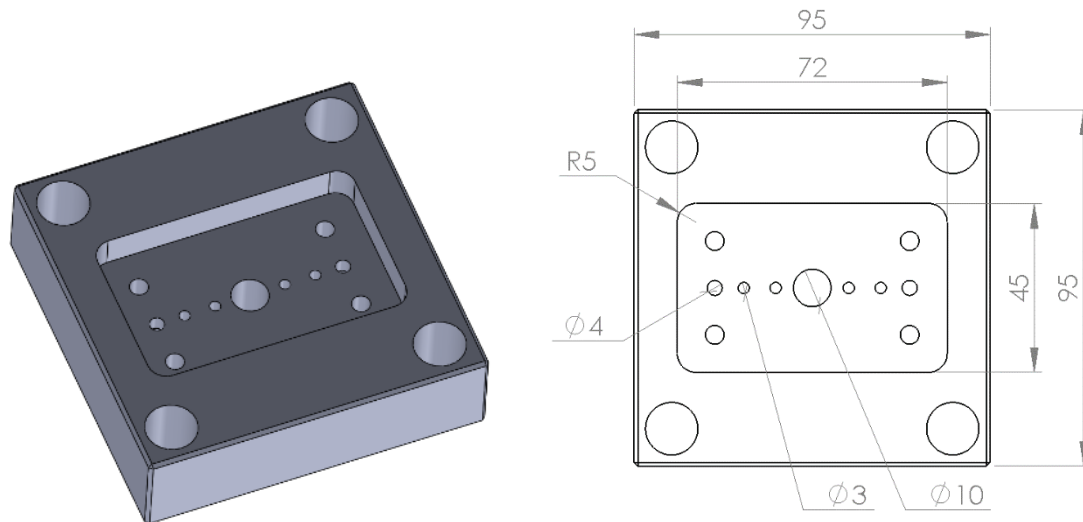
Esquerra: Model CAD del MUD. Dreta: Vista en planta del MUD (Font pròpia)
